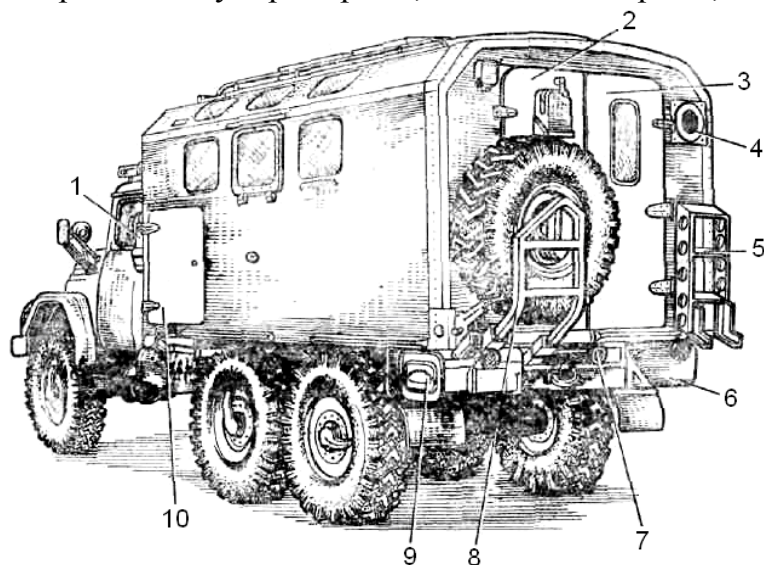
Общий вид мастерской сзади: 1 – огнетушитель; 2, 3 – створки двери; 4 – крышка люка дымовой трубы; 5 – трап; 6, 9 – багажные ящики; 7 – основание стрелы; 8 – кронштейн крепления запасного колеса; 10 – дверка левая
